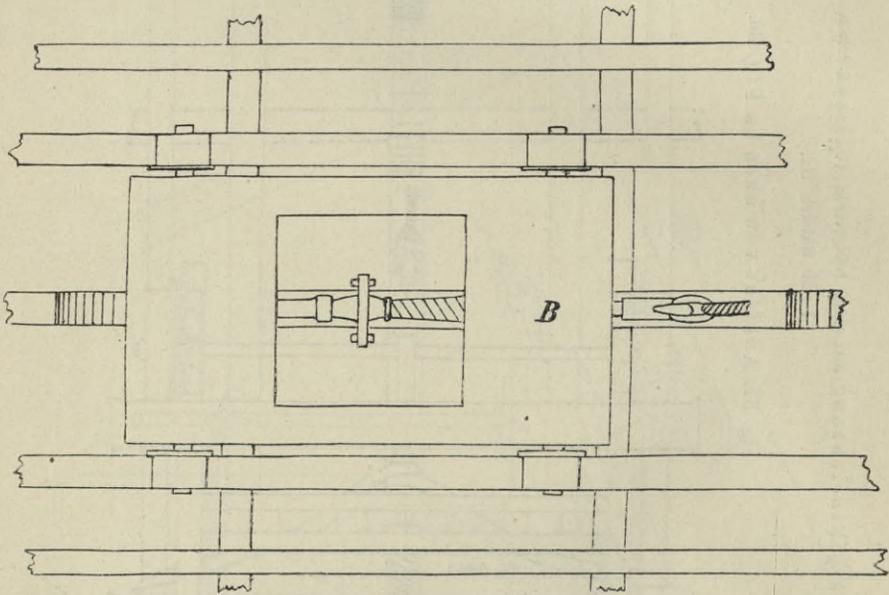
Ansicht des Gegengewichts-Wagens von Oben.
